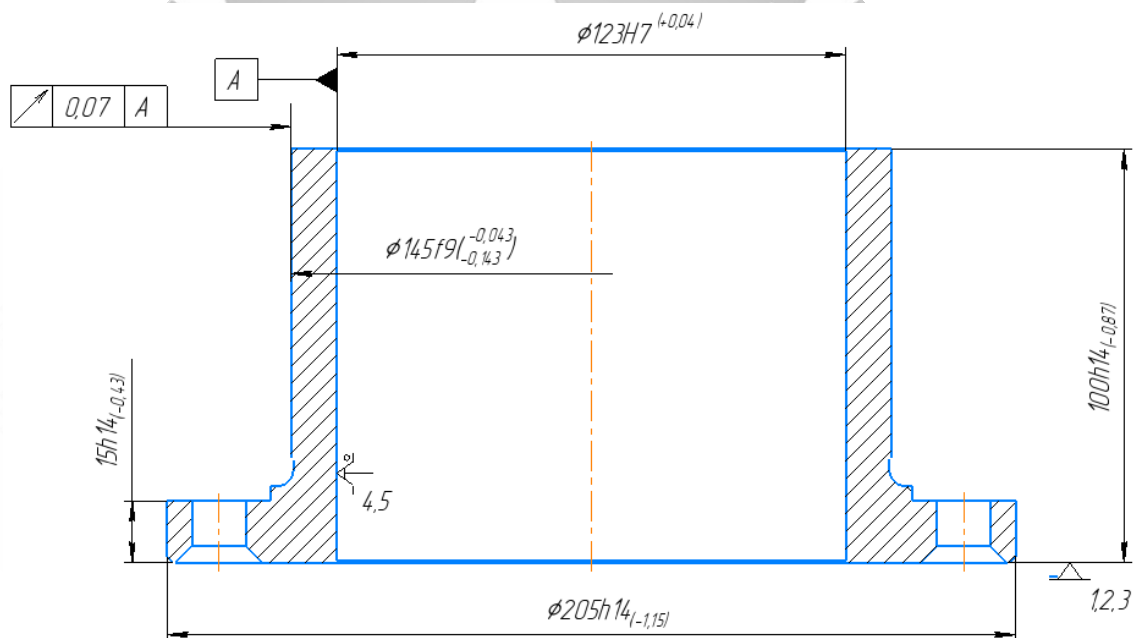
Схема базування та закріплення деталі на операції контролю
